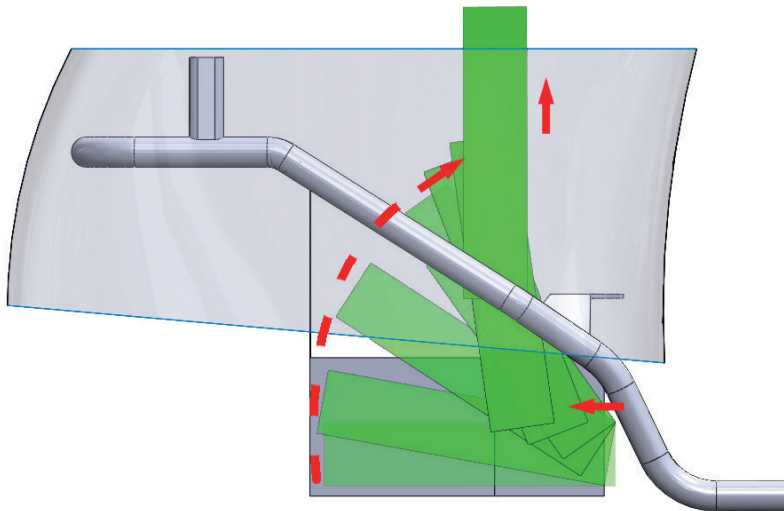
, De accu past door het frame, maar dient daarvoor wel gedraaid te worden tijdens het plaatsen.
